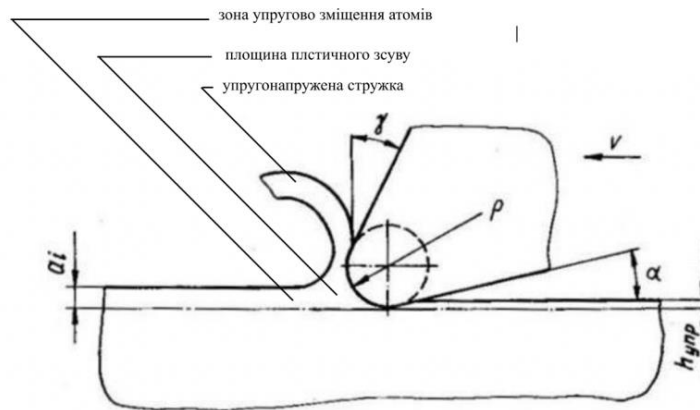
Схема врізання зуба фрези при швидкісному зубофрезеруванні
